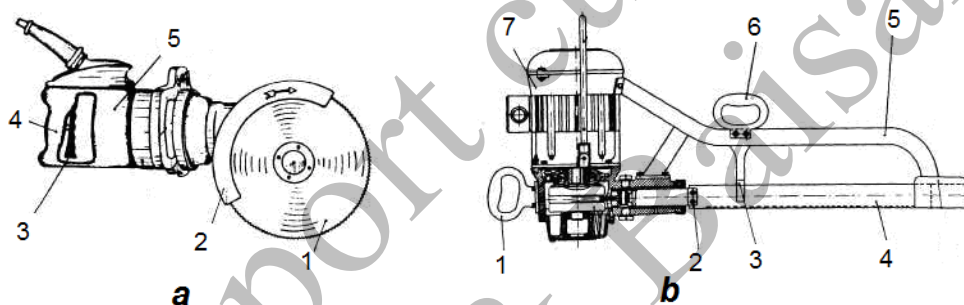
Fierăstrău mobil: a- circular: 1- disc tăiere; 2- apărătoare; 3- contactor; 4- mâner; 5- corp; b- lamelar: 1, 6- mâner; 2- punct de prindere lamă; 3- ghidaj; 4- pânză lamelară; 5- cadru; 7- motor electric.
